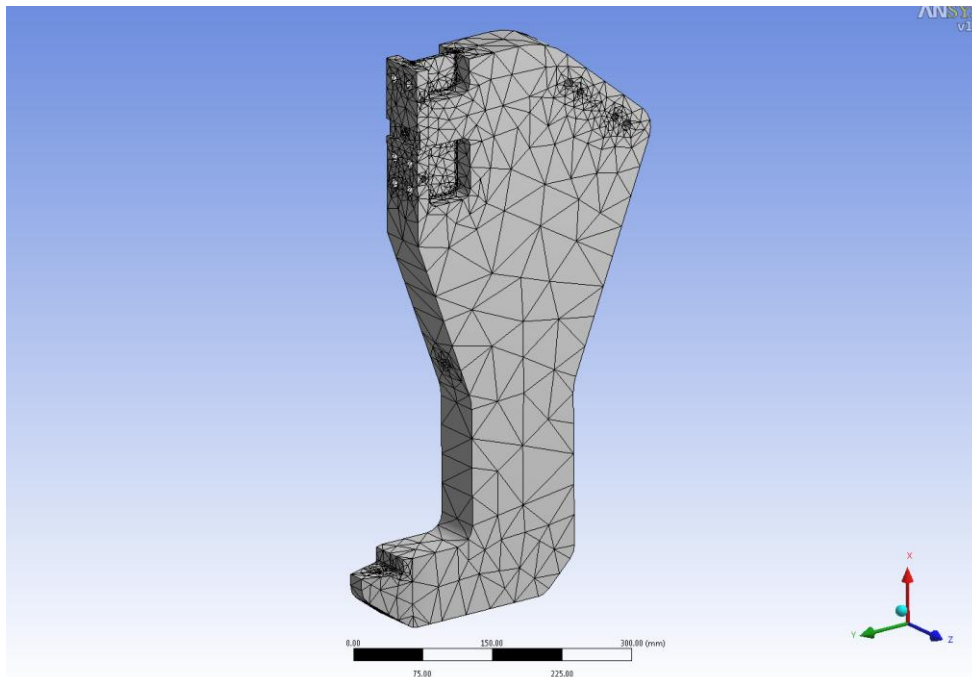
3D-Werkzeug aus CAD und Vollkörper vernetztes FE-Modell des C-Rahmens (ohne Antrieb und Clinchwerkzeug)
